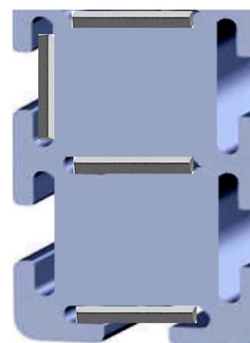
Алюминиевый корпус с подвижными сегментами.
